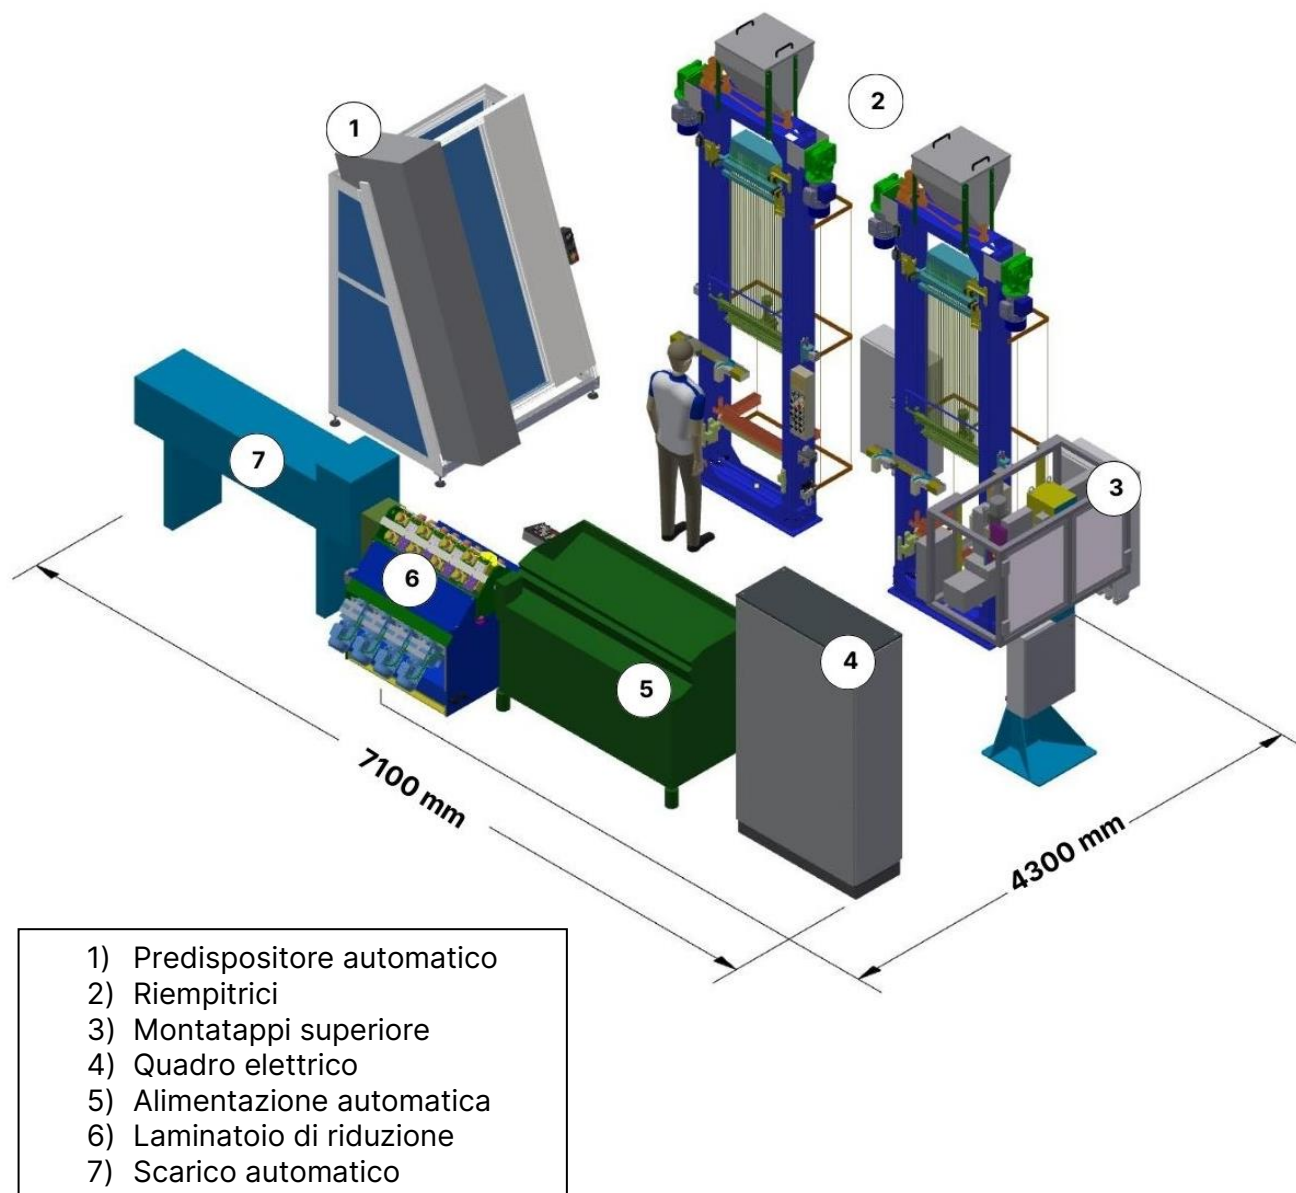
Ingombro in pianta del centro di riempitura con laminatoio di riduzione.
